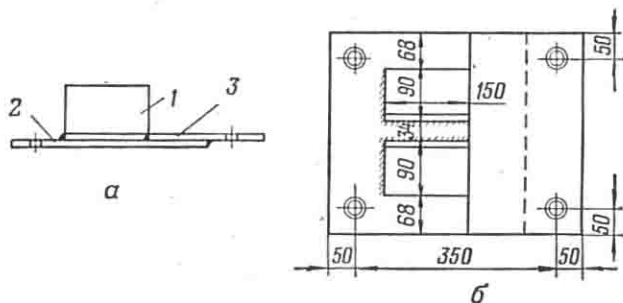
Правильная плита конструкции Н. С. Замкова:
